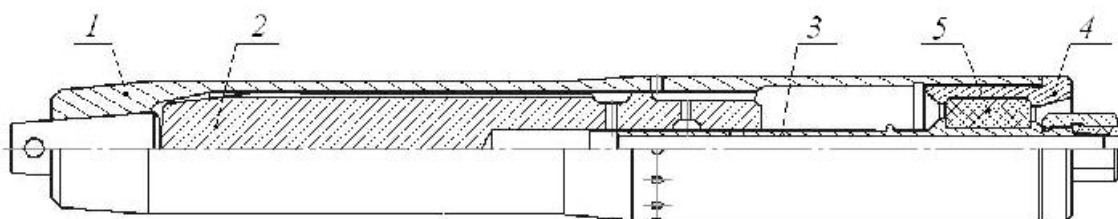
Общий вид экспериментального образца пневмоударного механизма с двумя управляемыми камерами: 1 – корпус с наковальней; 2 – ударник; 3 – патрубок; 4 – гайка; 5 – амортизатор
